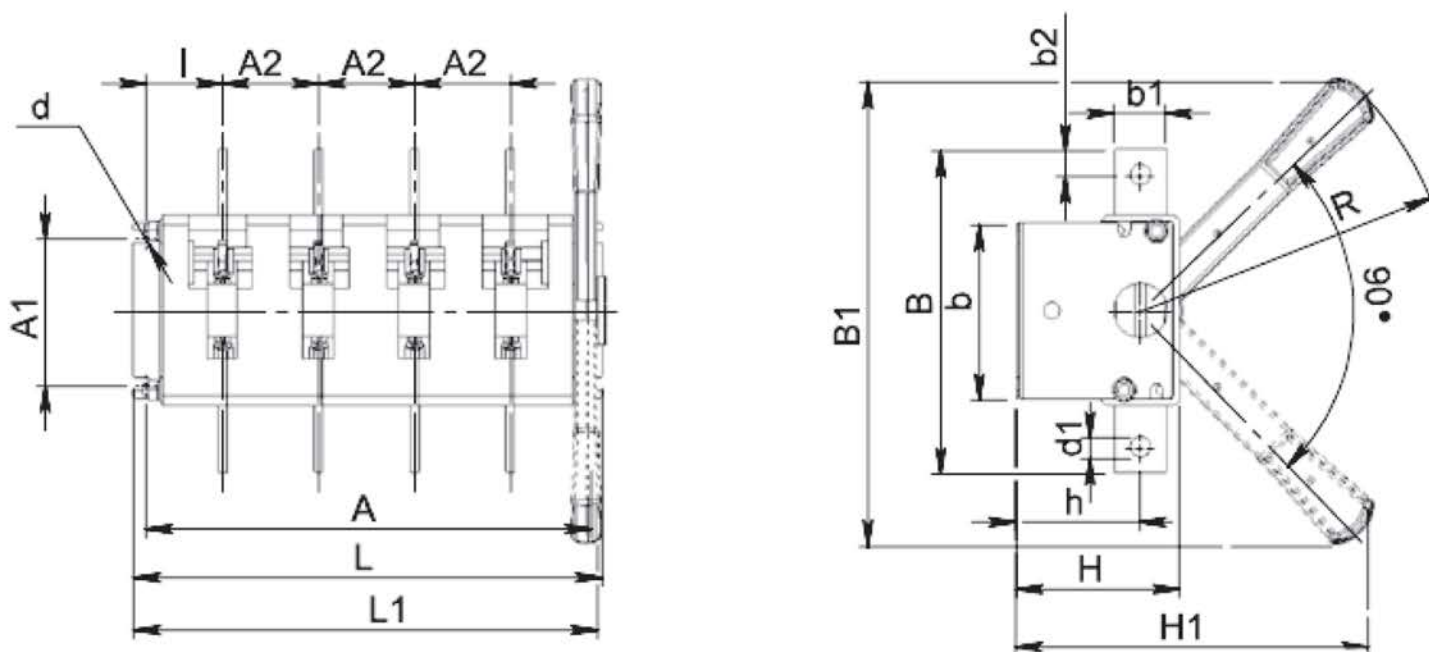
Выключатель-разъединитель четырехполюсный на одно направление с передней смещенной рукояткой.
